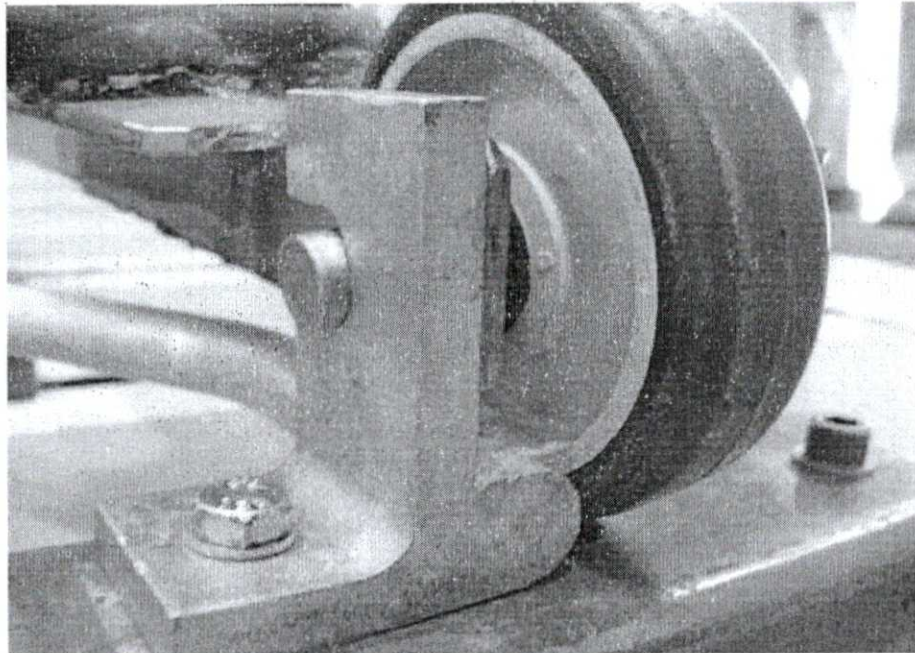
Lado esquerdo da amostra 3 após ensaio.
